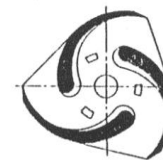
Offenes Dreikanalrad mit zylindrischen Schaufeln
